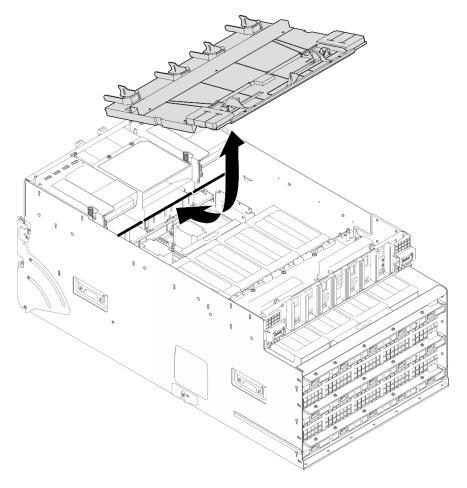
Instalación del marco del soporte del cable y del conjunto del deflector
